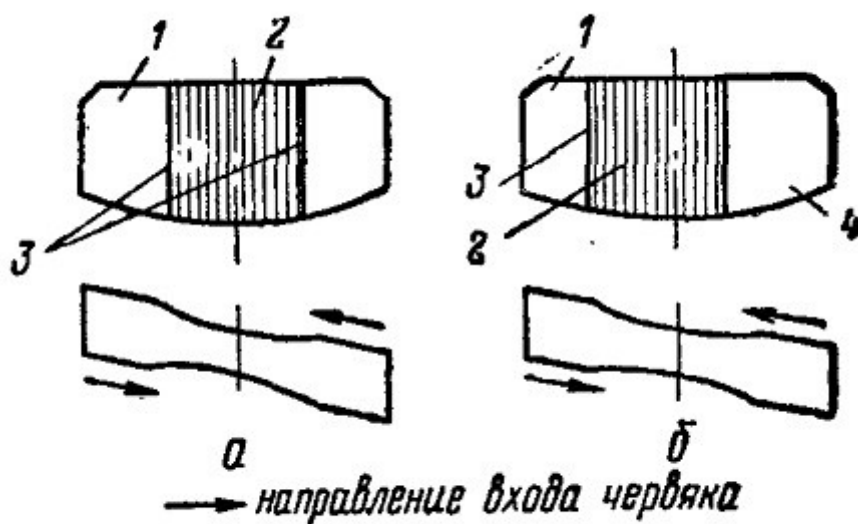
Зуб колеса новой передачи, нарезанный трехзубой фрезой-летучкой (а) и глобоидной фрезой (б):
